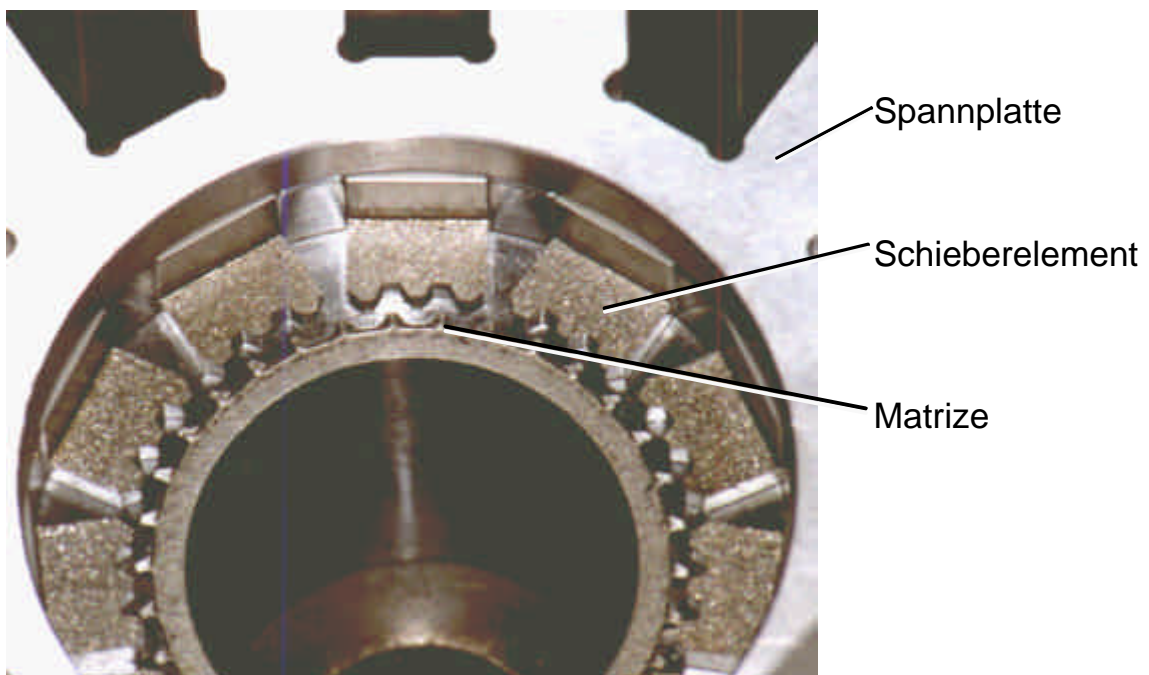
Werkzeugsystem der zweiten Umformstufe (Detailansicht)
